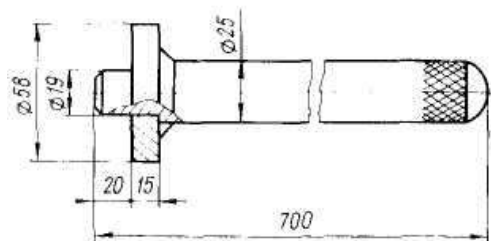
Оправка для выпрессовки и запрессовки подушки со средним подшипником в сборе
